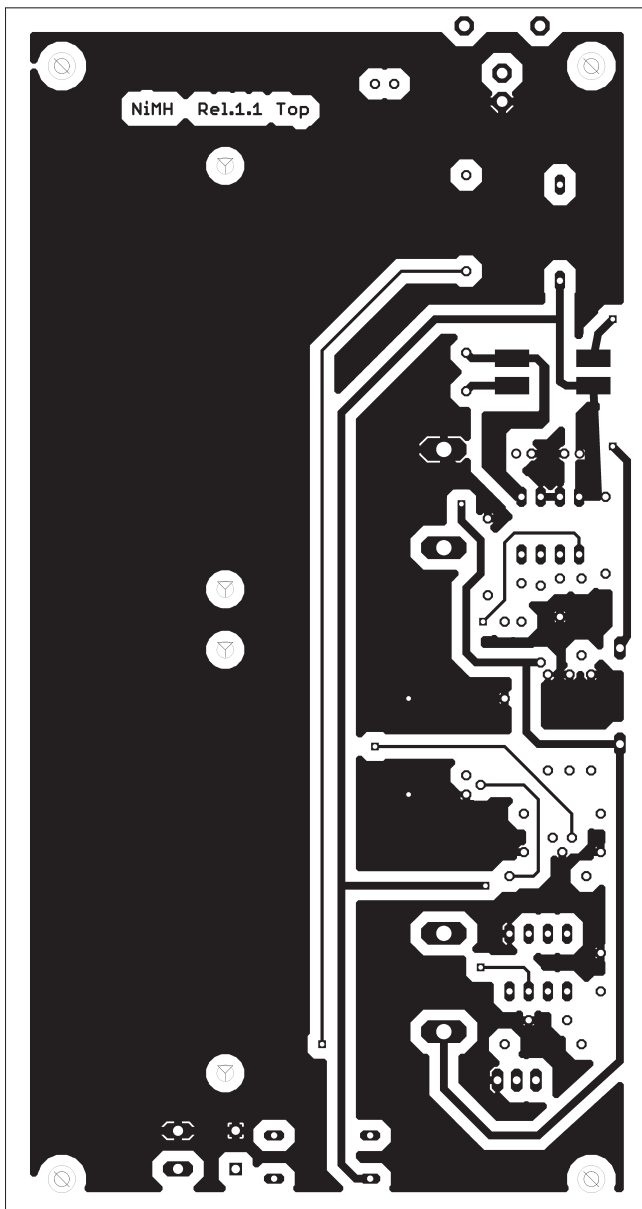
Layout der Bestückungsseite der Ladebaugruppe
